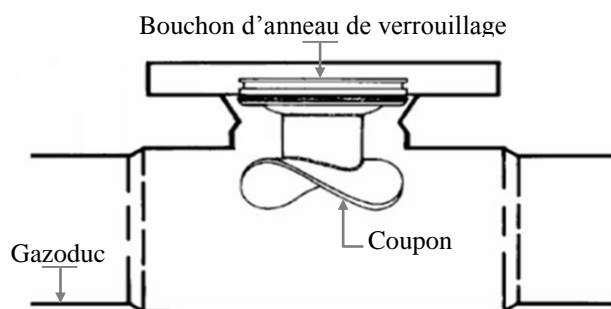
Installation des bouchons d'anneau de verrouillage
